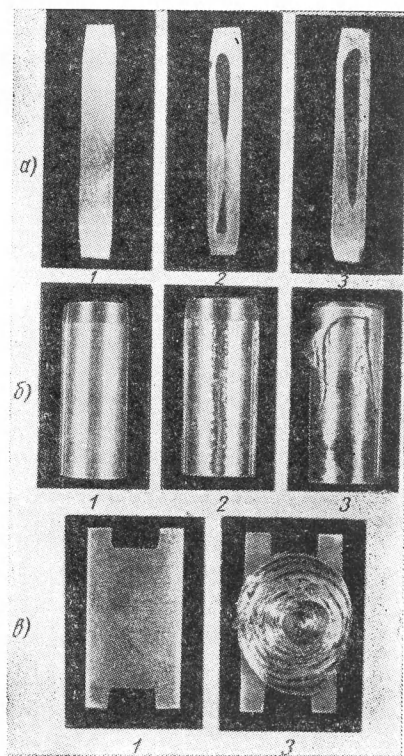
Быстроизнашиваемые детали обкатной головки:
